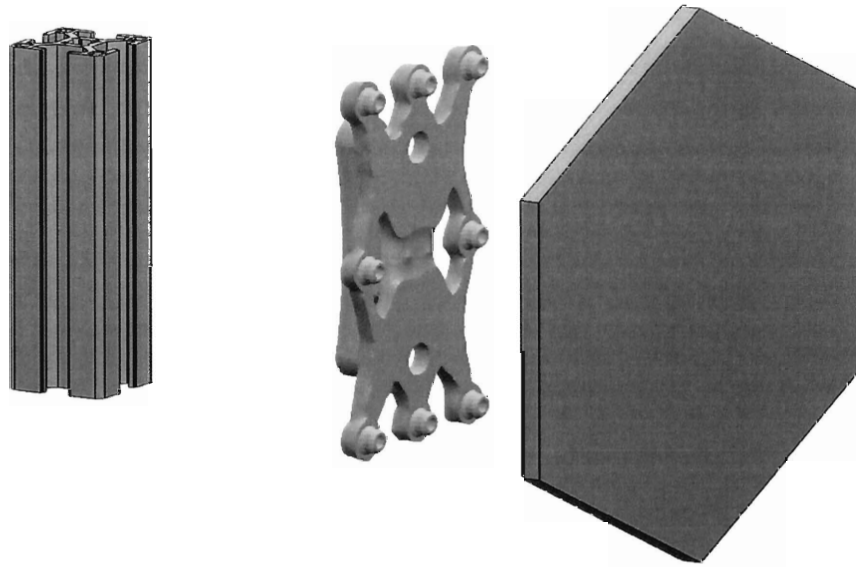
Vedere izometrică explodată ansamblu – TIP 2
